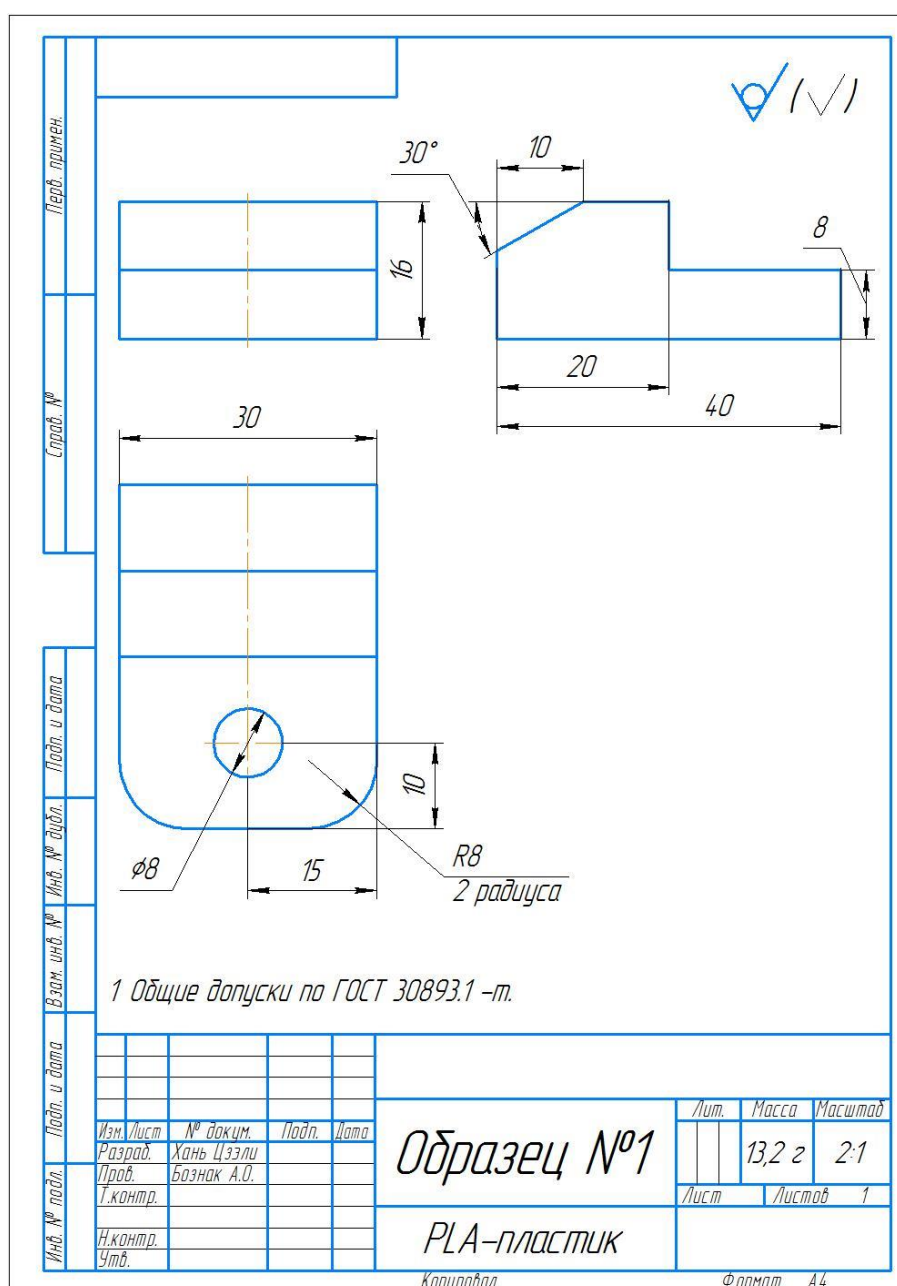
Чертеж детали «Образец №1»
